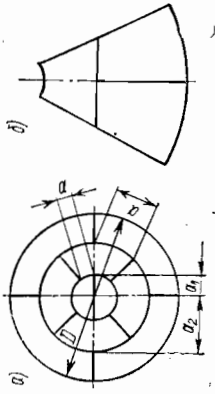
Расположение стыков в полушаровых днищах, изготовляемых из отдельных частей: а — пример расположения сварных швов в днище; б — пример расположения сварных швов в плоской заготовке лепестка
